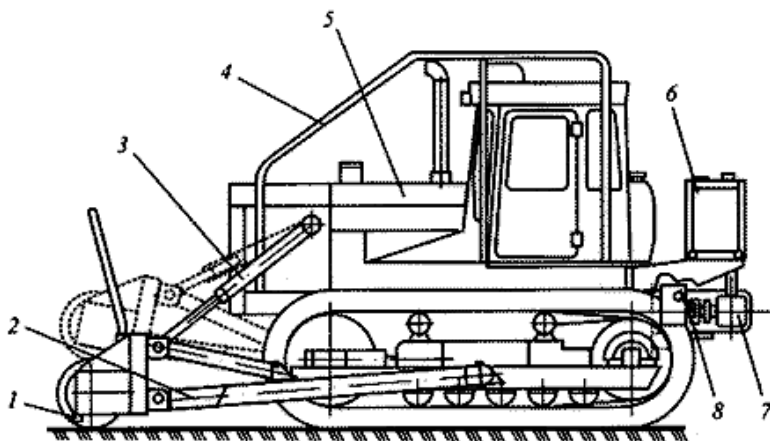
Кусторез с фрезерным рабочим органом:
